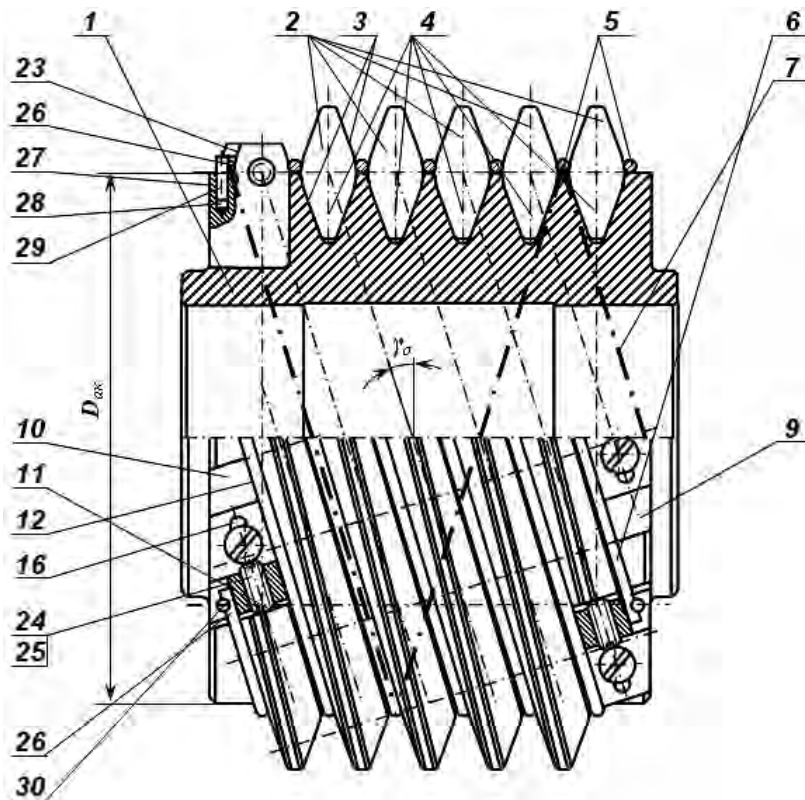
Збірна черв'ячна фреза з пружинним кріпленням ріжучих пластин і клинових вставок між витками її корпусу
